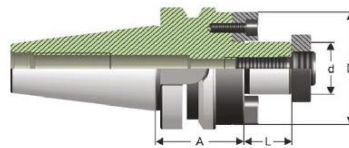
Оправка для торцевої фрези JIS B 6339 [15, С-12]
